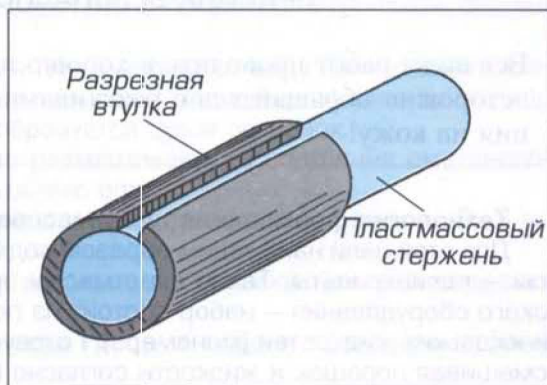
Разрезная втулка для крепления пластмассовой заготовки в патроне станка
